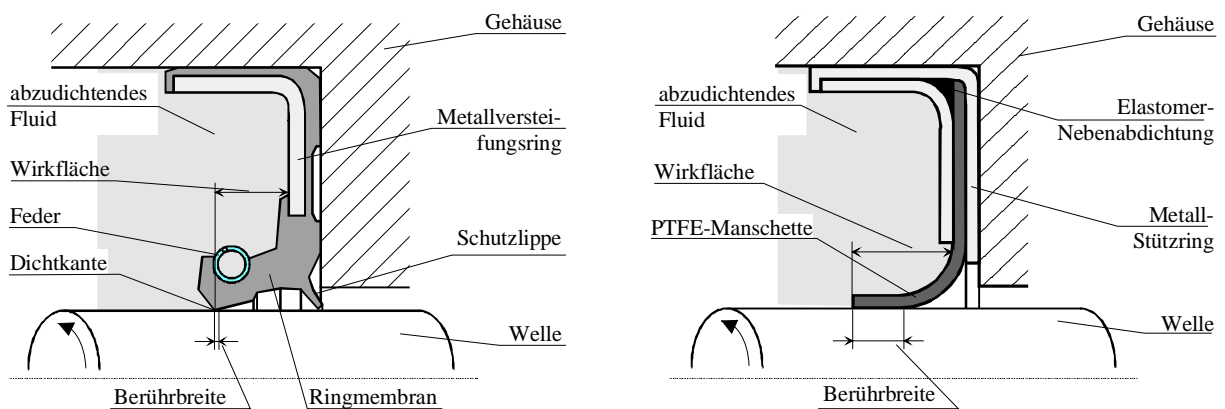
Prinzipbild eines Radial-Wellendichtrings aus Elastomer (links) und eines Radial-Wellendichtrings aus PTFE (rechts)
